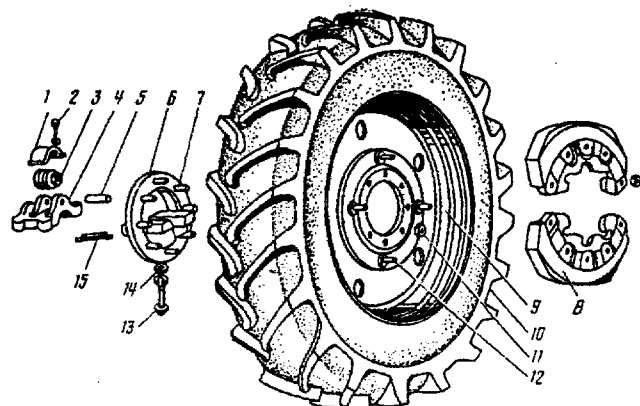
Заднее ведущее колесо тракторов семейства МТЗ: 1 – крышка винта; 2 – болт; 3 – регулировочный винт; 4 – вкладыш ступицы; 5 – ось регулировочного винта; 6 – ступица; 7 – болт; 8 – балластный груз; 9 – обод; 10 – шина; 11 – гайка; 12 – болт крепления балластного груза; 13 – болт ступицы; 14 – сферическая шайба; 15 – шпонка
